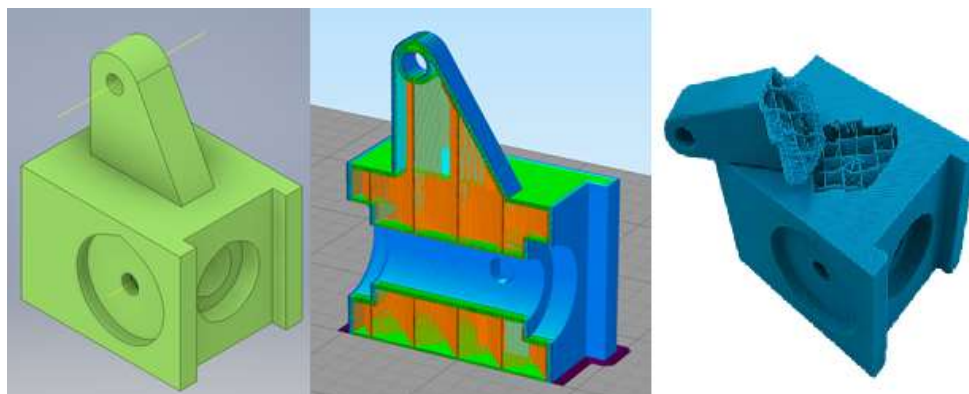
Модель детали «кулак», разрез симуляции детали со стандартными настройками печати и реальная деталь
